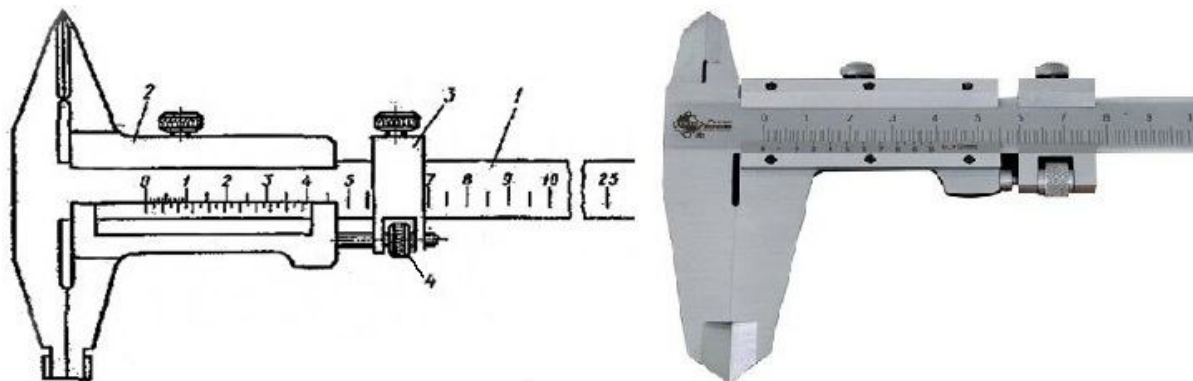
Устройство штангенциркуля: 1 – линейка; 2 – рамка; 3 – стопорная рамка; 4 – гайка микроподачи рамки
